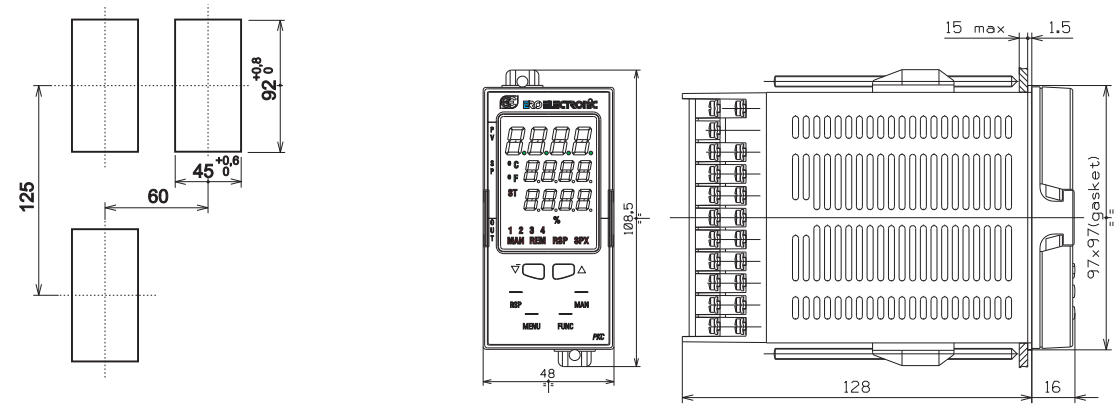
A DIMENSIONI E FORATURA PER PKC
